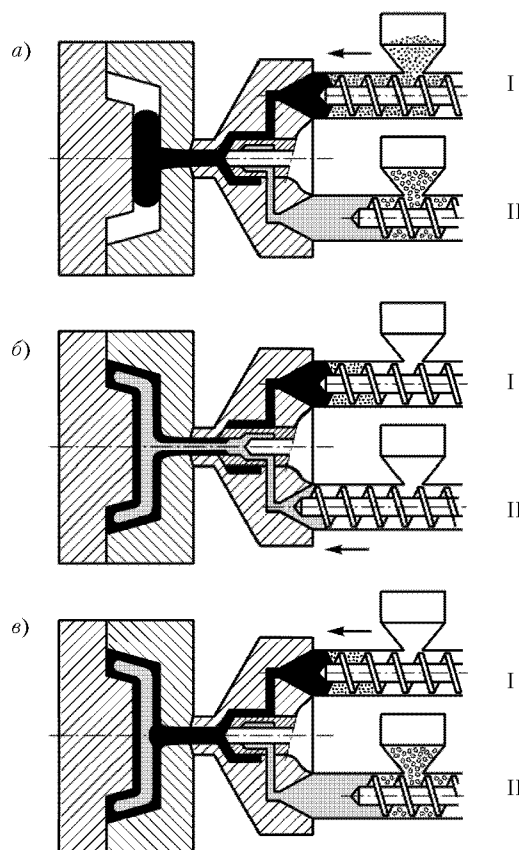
Схема сэндвич-литья двухслойного изделия
